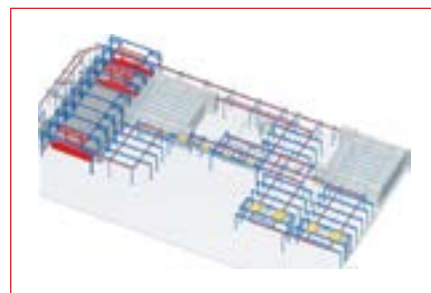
Линия катодного грунтования и порошковой окраски металлоконструкций на базе конвейера Power & Free
